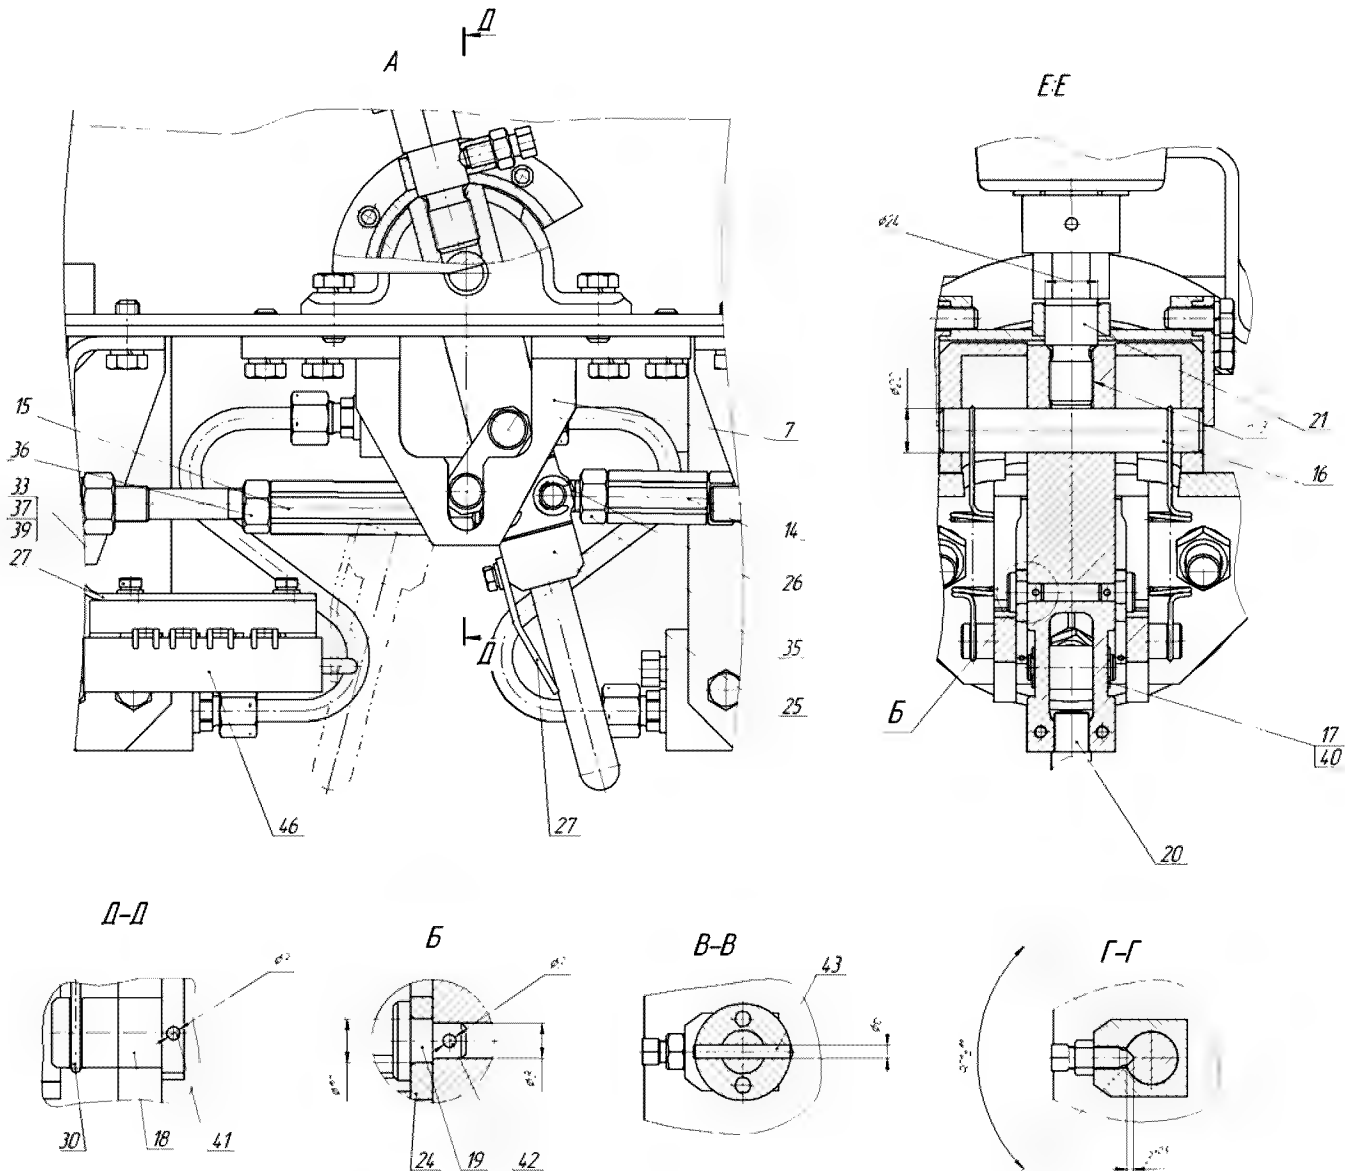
Устройство разъединителя РЛД-3,0/1,85
